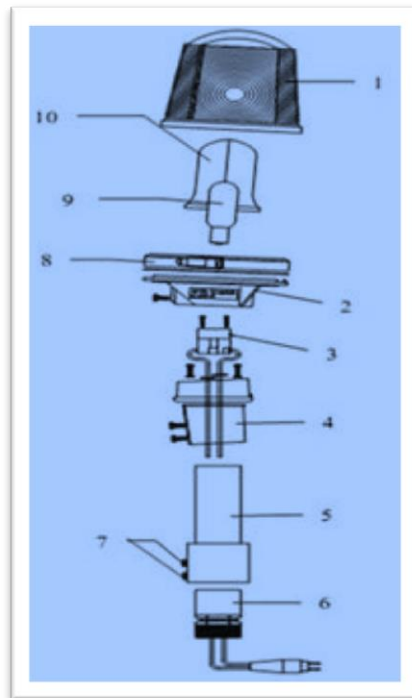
Luminaria elevada montada en placa y elemento frangible
